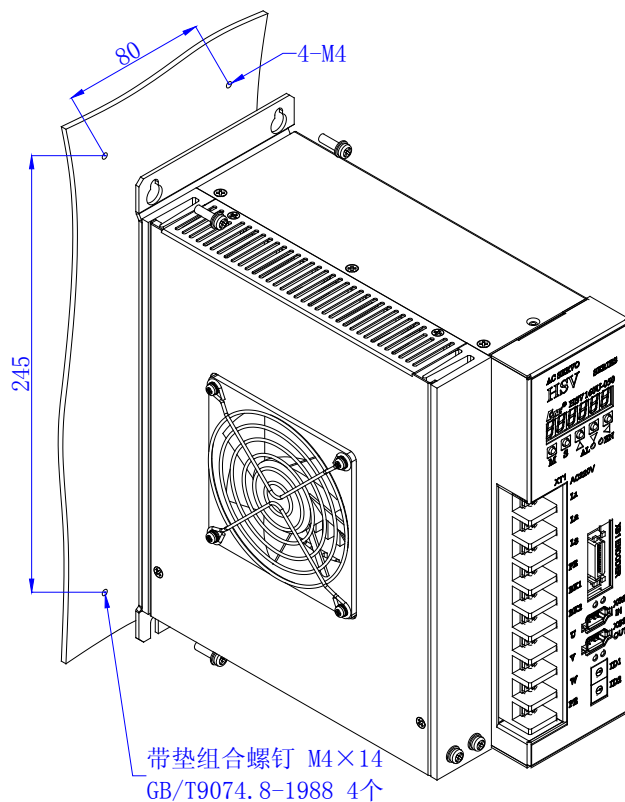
HSV-160U-050、075 驱动单元底板安装示意图(单位: mm)
